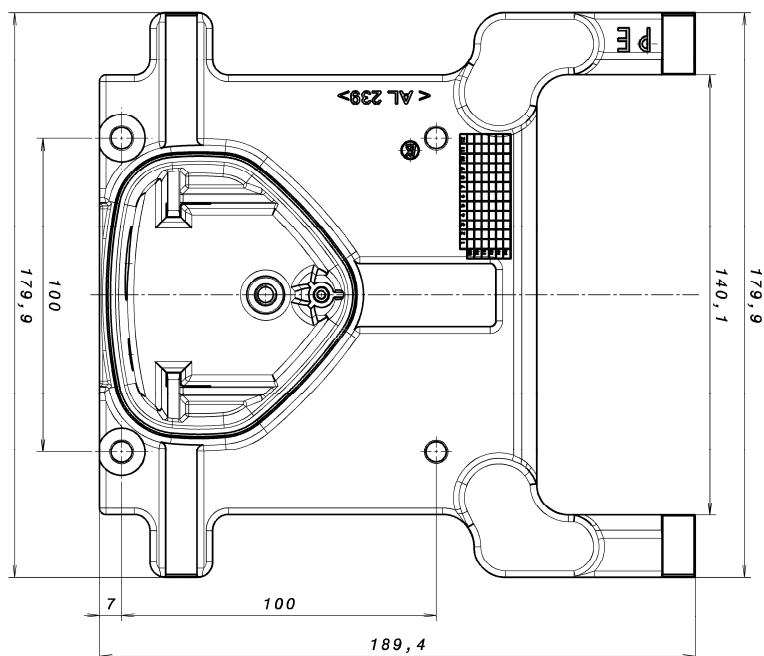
Bohrbild Standard-Wand- Adapterplatte BG C
